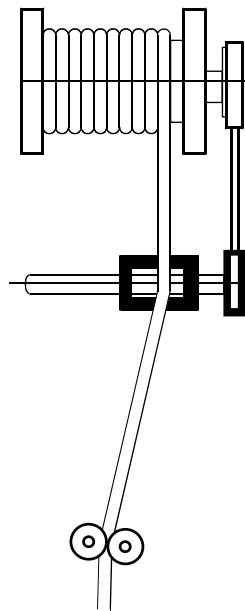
Vista superior del conjunto bobina (arriba), posicionador (medio) y entrada de cable (abajo)
